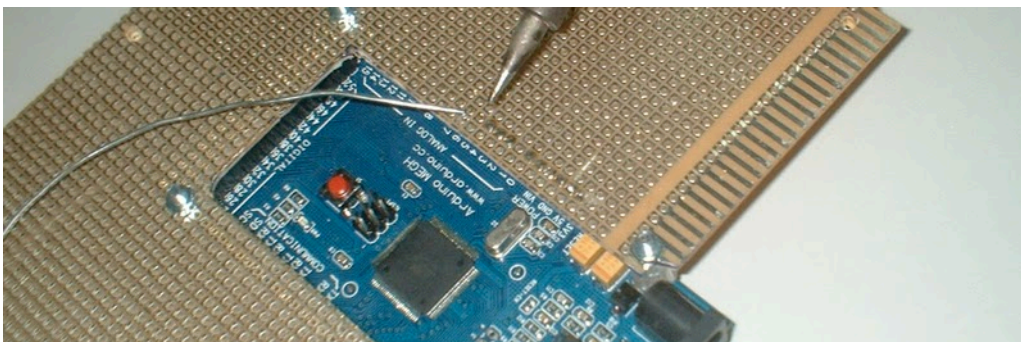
Soldadura do Arduino à placa perfurada
